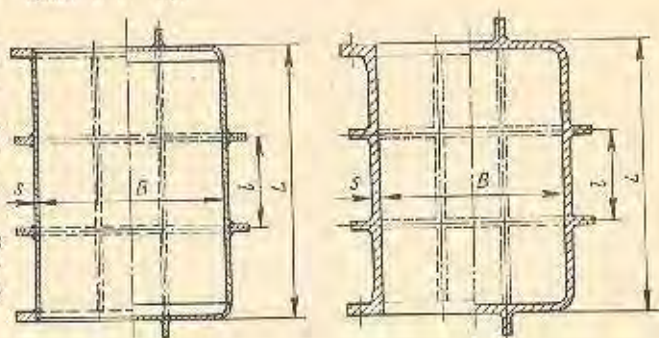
Основные типовые конструкции коробчатых обечайки химических аппаратов: I — сварные; II — литые
